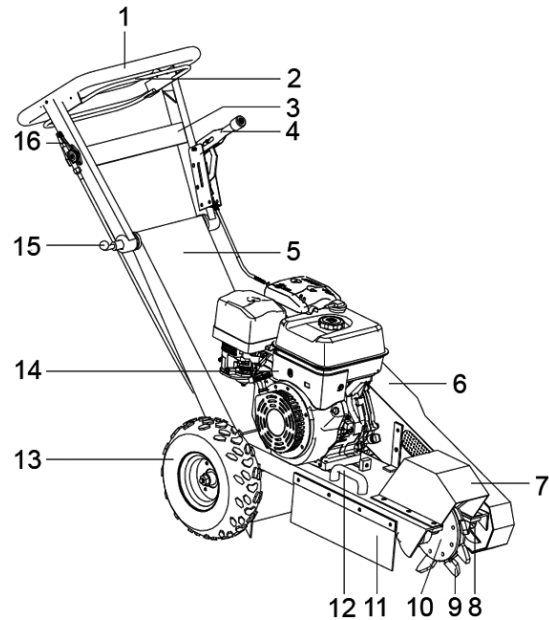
Gesamtmaschine Wurzelfräse BSF-15
